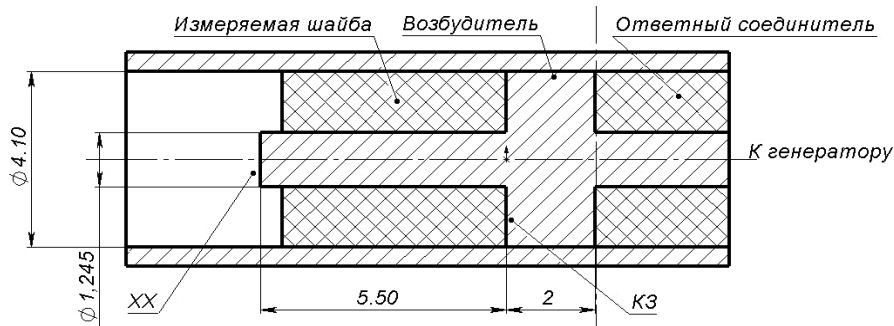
Коаксиальный четвертьволновый резонатор для шайб соединителей типа SMA
